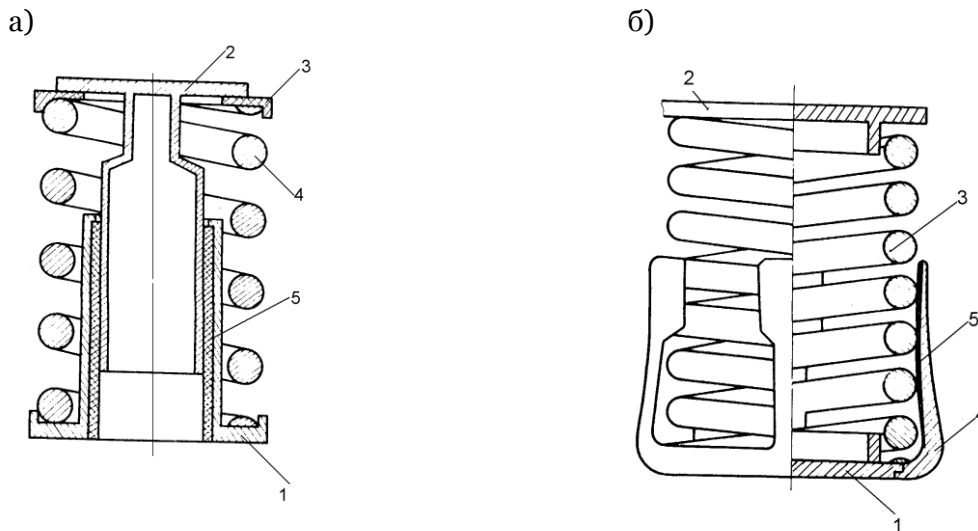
Общий вид виброизолирующего устройства подвески сиденья с демпфером сухого трения: а) втулочного типа, б) с лепестками
